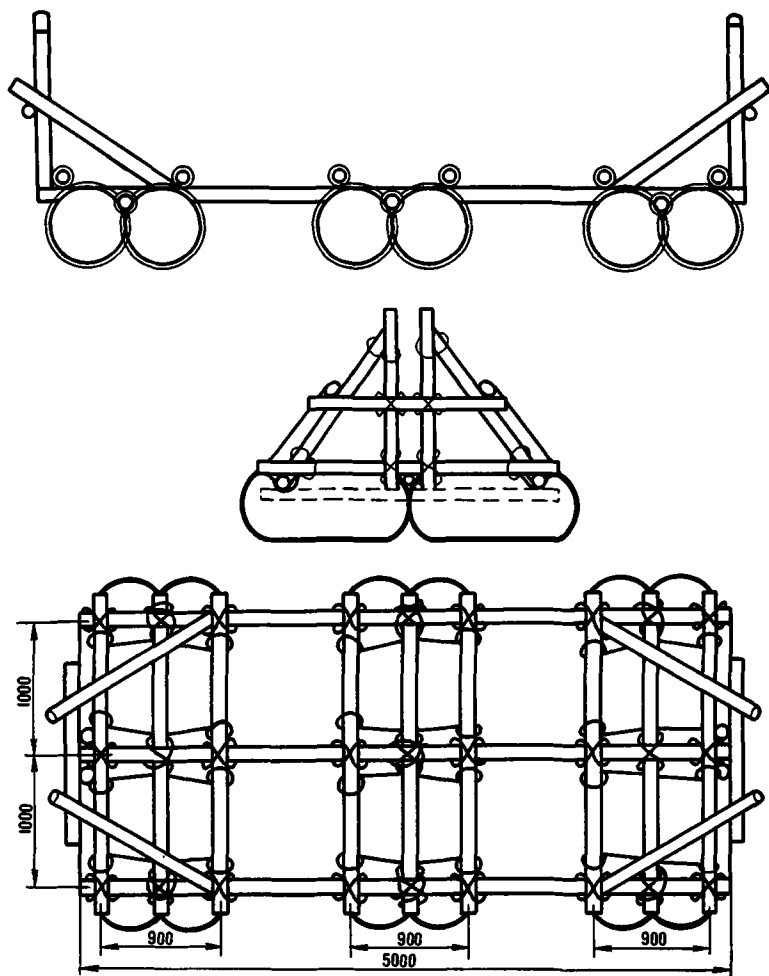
Плот с поперечно расположенными поллавками конструкции А. Чернышева
